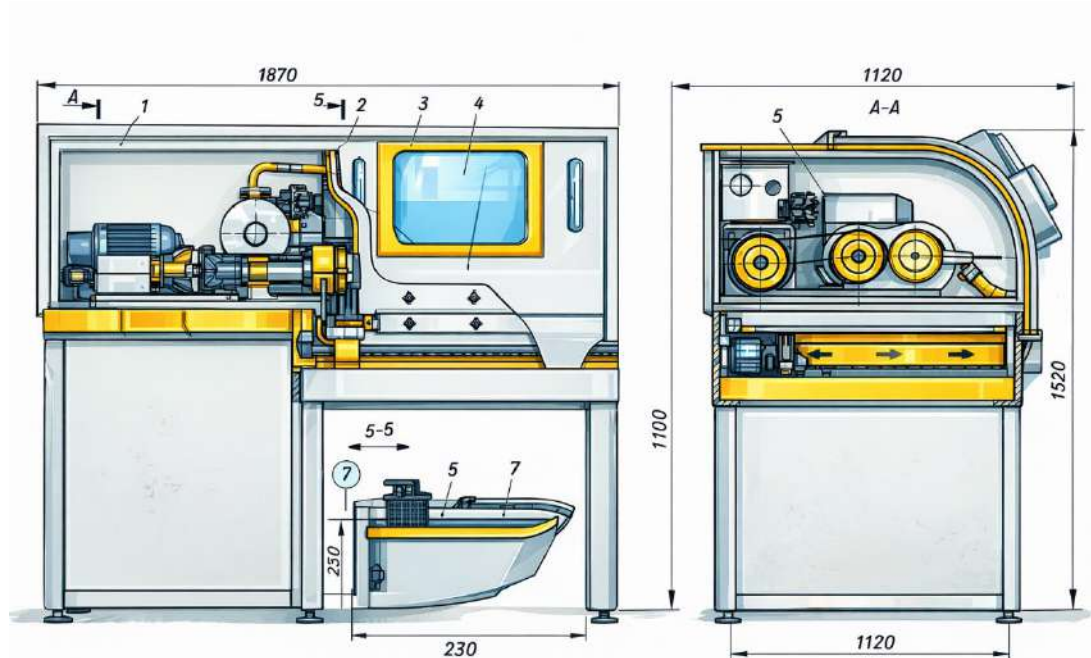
Установка для відновлення деталей плазмовим напиленням
